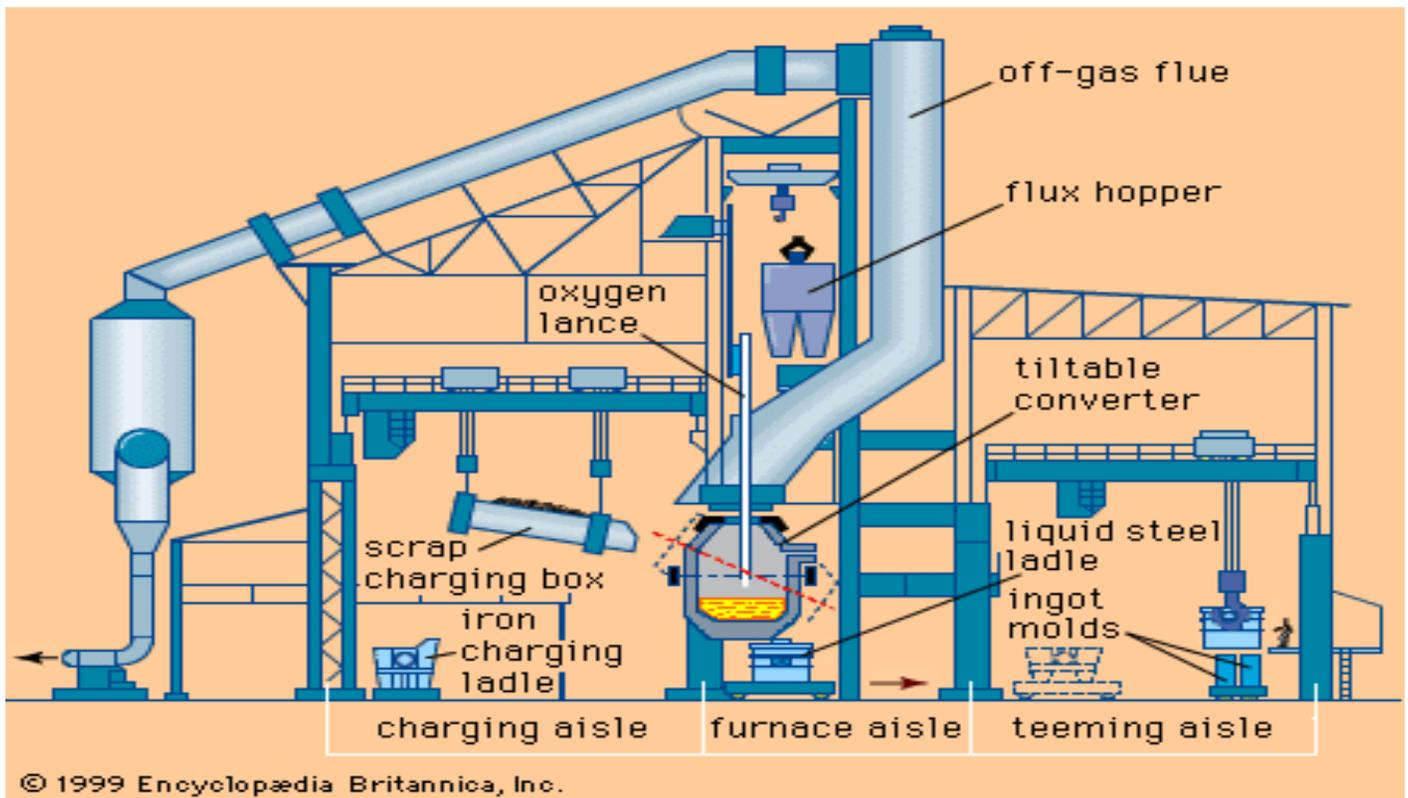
Vista seccional de la instalación auxiliar de una planta para BOF.
